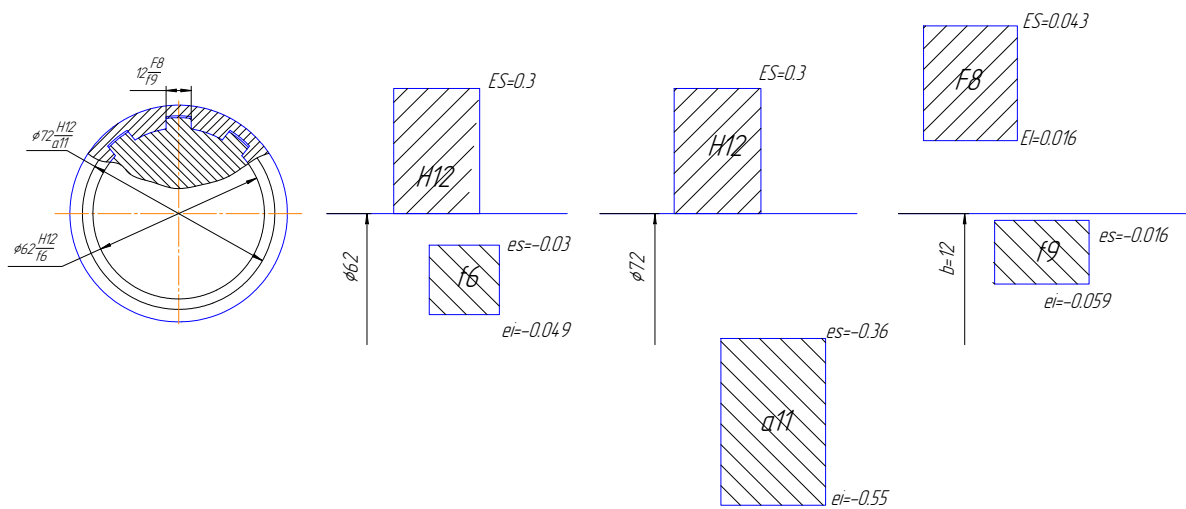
Схема розташування полів допусків у шліцьовому з'єднанні
